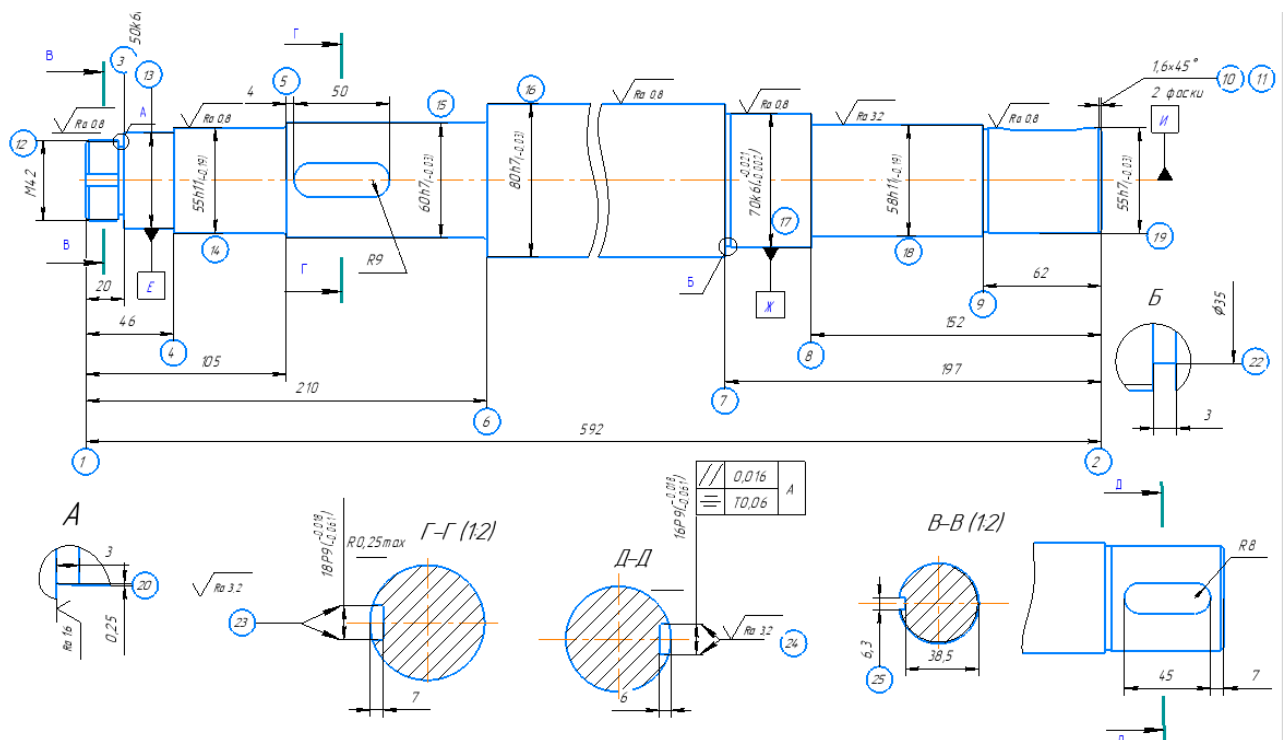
Основні оброблювані поверхні деталі «Вал черв'ячного редуктора»
